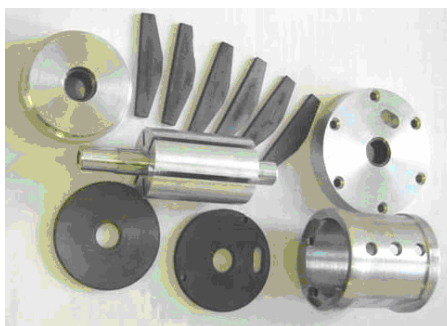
Опытный образец реверсивного пластинчатого ПМ с полиамидными пластинами и металлофторопластовыми подшипниками.
